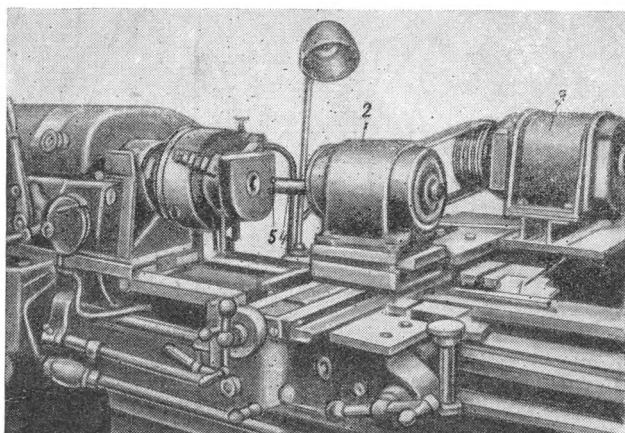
Приспособление для вихревого нарезания внутренней резьбы.
